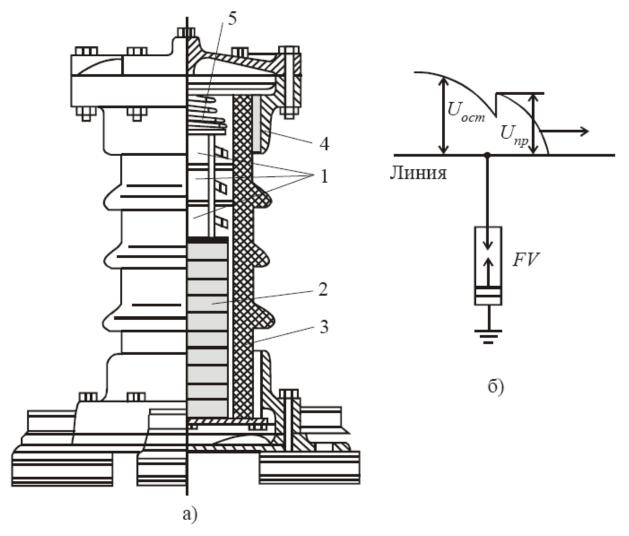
Вентильный разрядник: а) общий вид; б) схема включения. 1 – искровые промежутки; 2 – вилитовые (тервитовые) диски; 3 – фарфоровый корпус; 4 – крышка; 5 – пружина.
